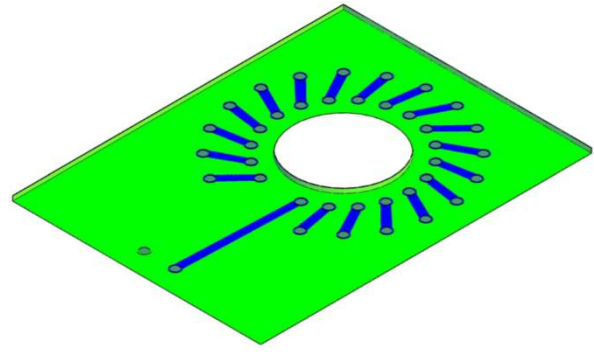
PCB em 3D parte inferior. (Autoria própria)
